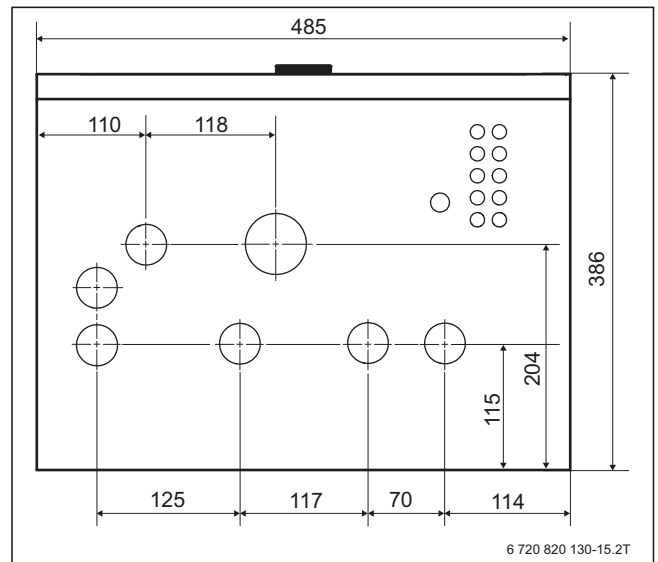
Abmessungen IDU-8/14 iB (Ansicht von unten; Maße in mm)
